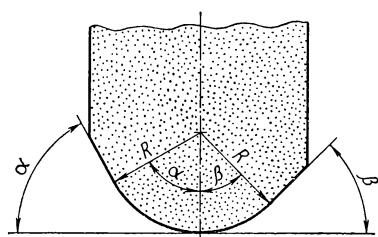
Профиль, заправляемый с помощью приспособления на круглошлифовальном станке
